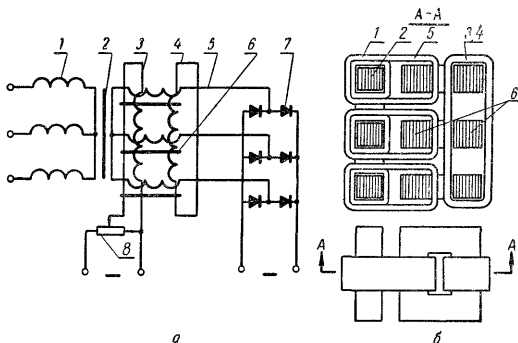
Схема трехфазного сварочного преобразователя типа СПС-300 с селеновыми выпрямителями:
